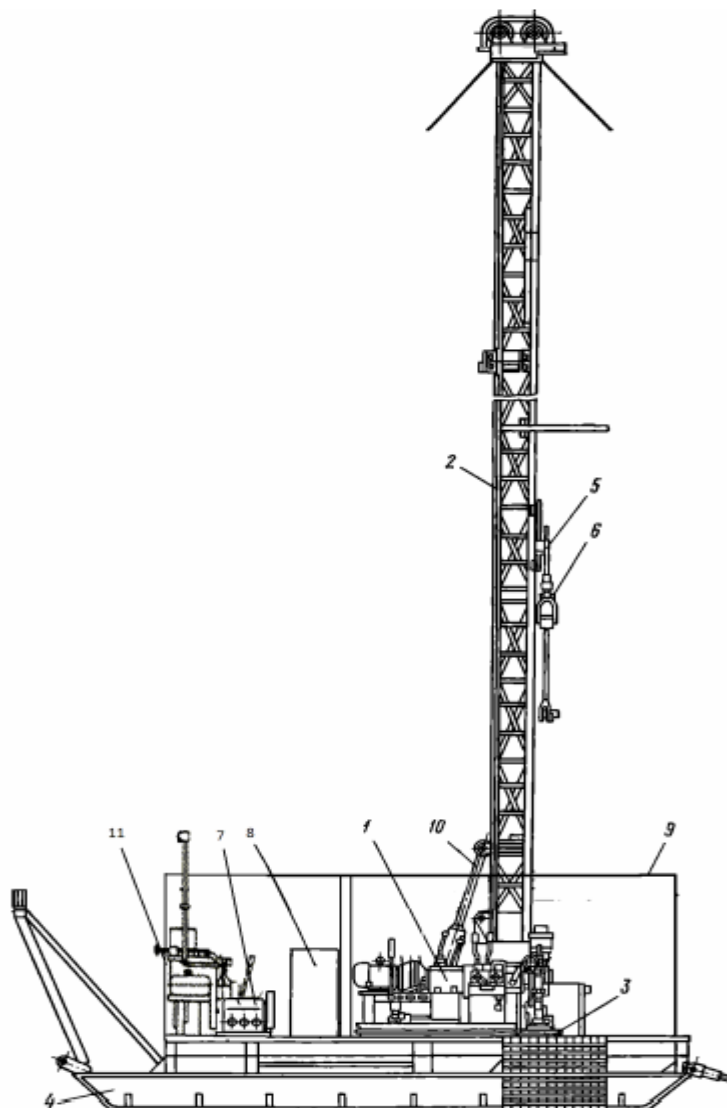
Передвижная буровая установка УКБ-200/300: 1 – буровой станок; 2 – мачта; 3 – труборазворот; 4 – санное основание; 5 – каретка; 6 – полуавтоматический элеватор; 7 – буровой насос; 8 – электрический шкаф; 9 – укрытие; 10 – гидроцилиндр; 11 – дизель-генератор
